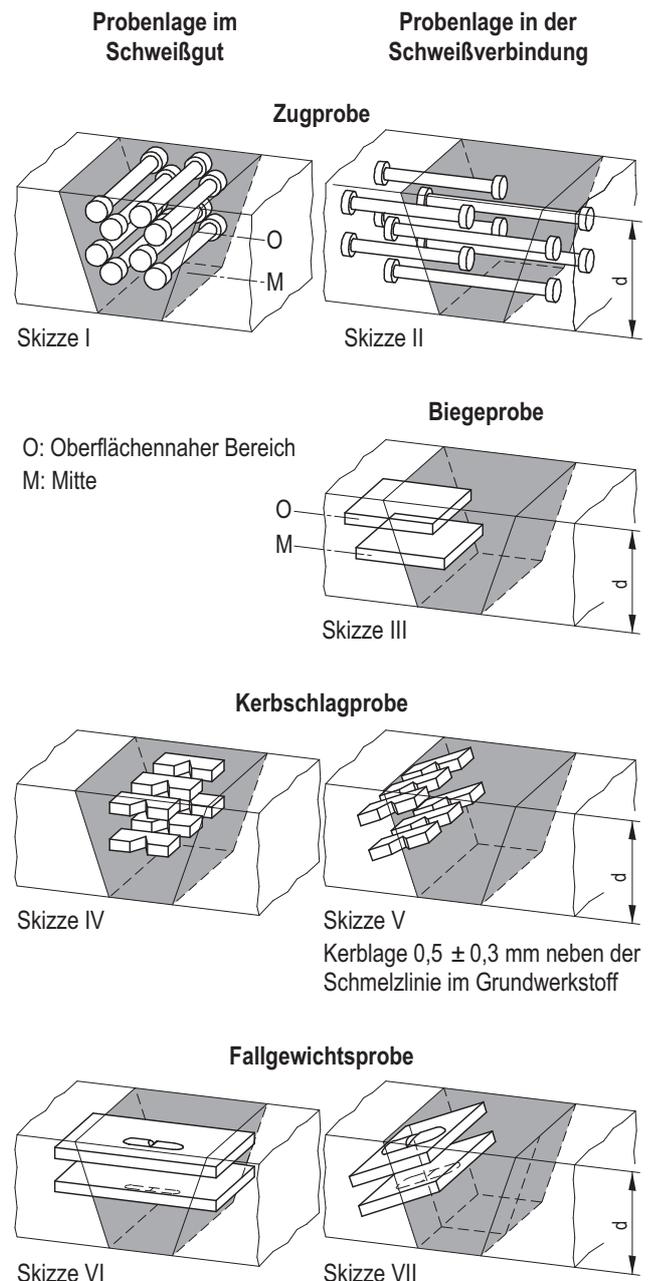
Probenentnahme bei Verfahrensprüfungen für Durchbruchschweißungen
